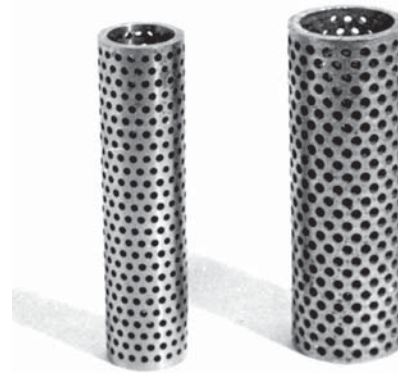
Матрицы для гидродинамической пробивки отверстий: слева – для варианта нагружения заготовки снаружи, справа – для нагружения такой же заготовки давлением изнутри
